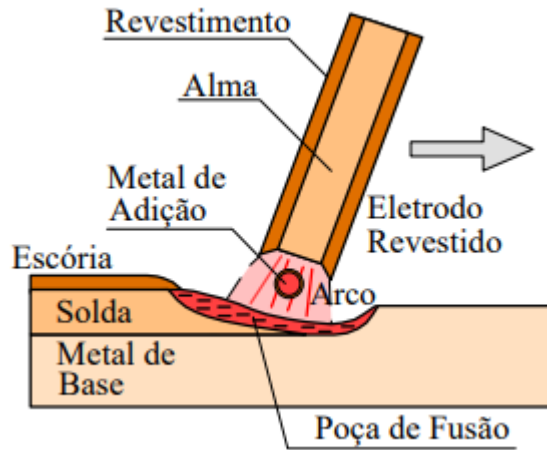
Desenho esquemático do processo de soldagem por eletrodo revestido.
